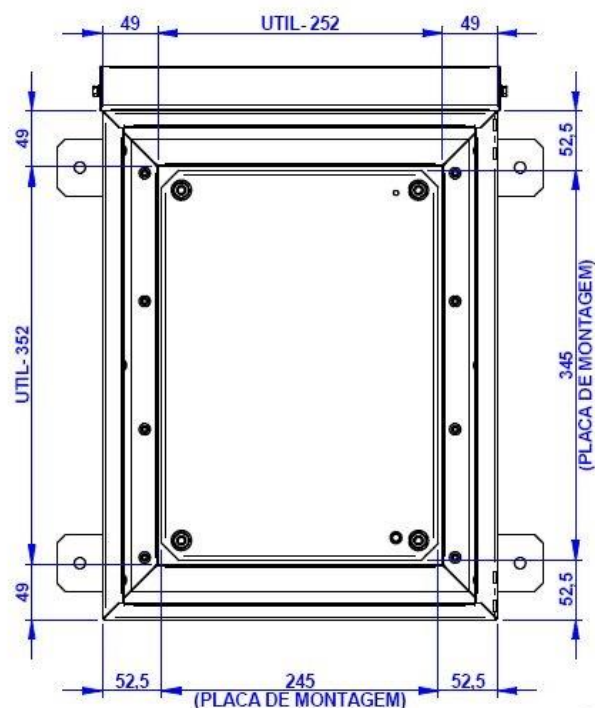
Dimensionamento para montagem (cotas em milímetros)
